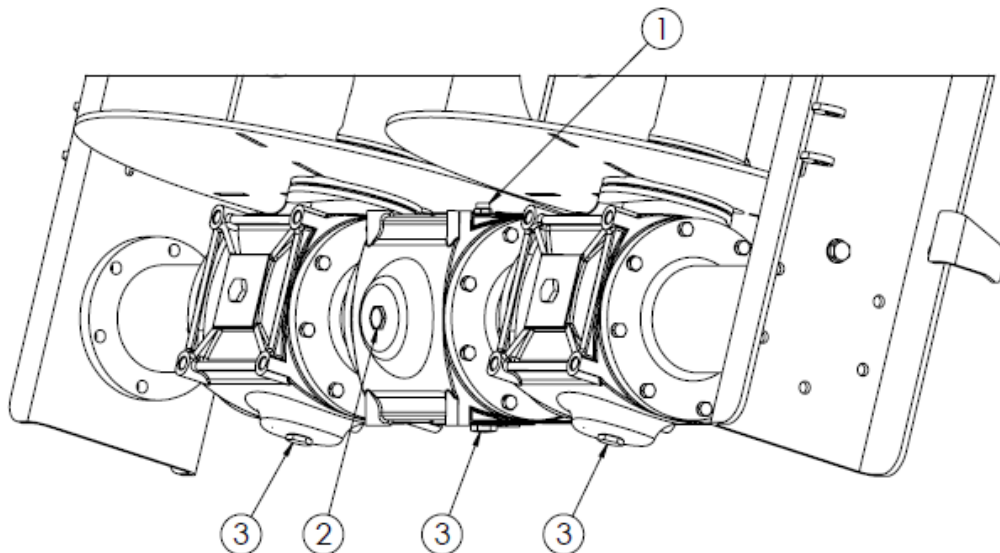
Точки контроля уровня масла редуктора адаптера.
